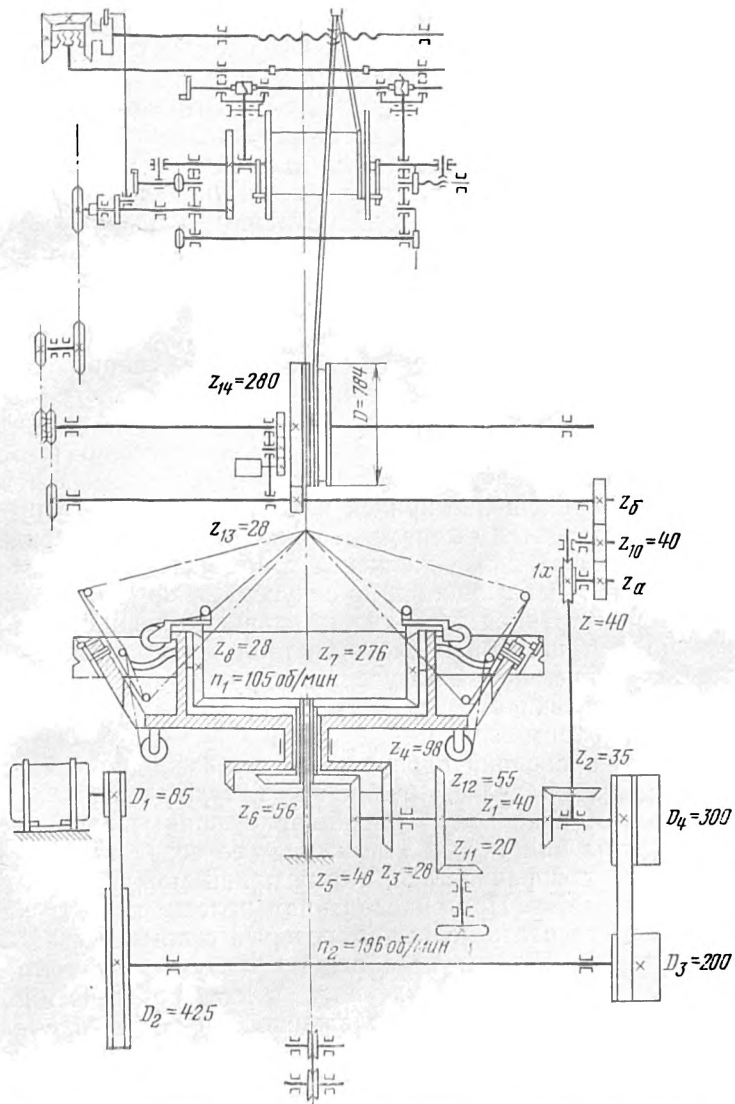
Кинематическая схема оплеточной машины карусельного типа ОПК-24-Э.
